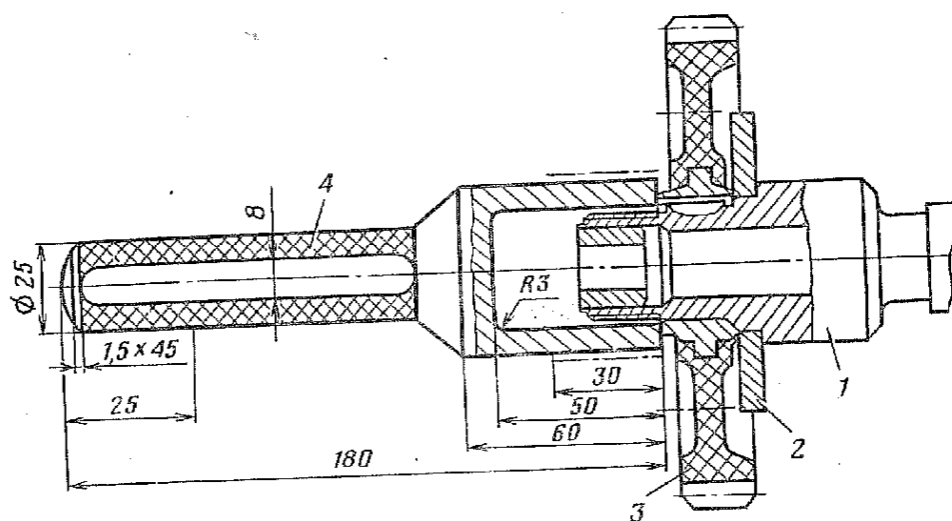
Оправка для напрессовки шестерни распределительного вала:
